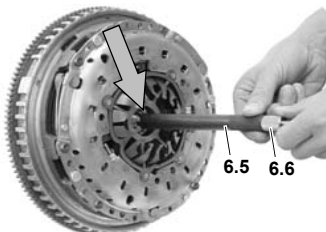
Dévisser les vis de fixation du mécanisme d'embrayage, les remplacer en vissant les goujons, monter le précompresseur d'embrayage.
